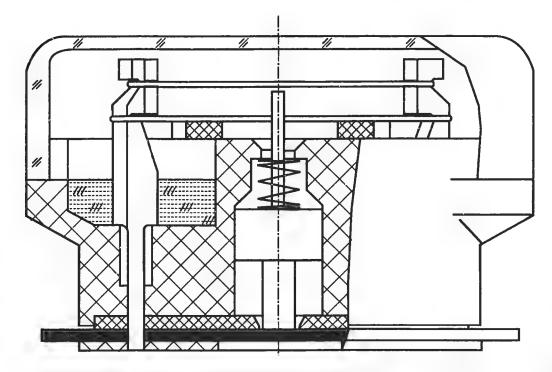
Предохранители с контролем срабатывания двухниточный, черт. 24714-00-00-08...-15
